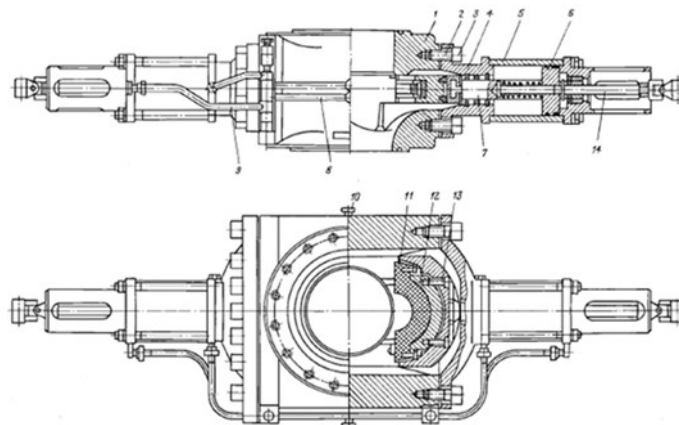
Устройство плашечного превентора ППГ [18-20]
